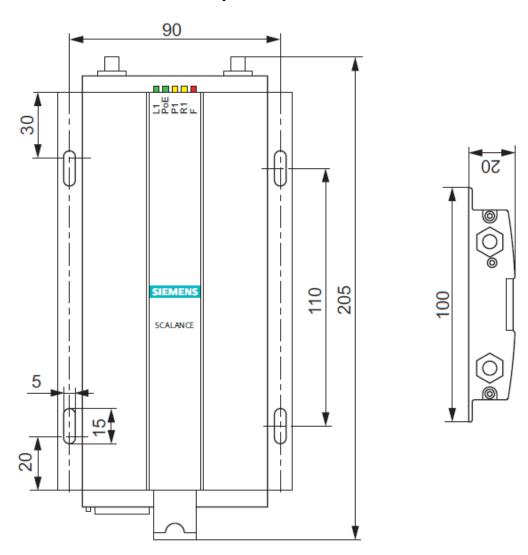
Dimensiones técnicas de los SCALANCE W784-1 y W746-1
